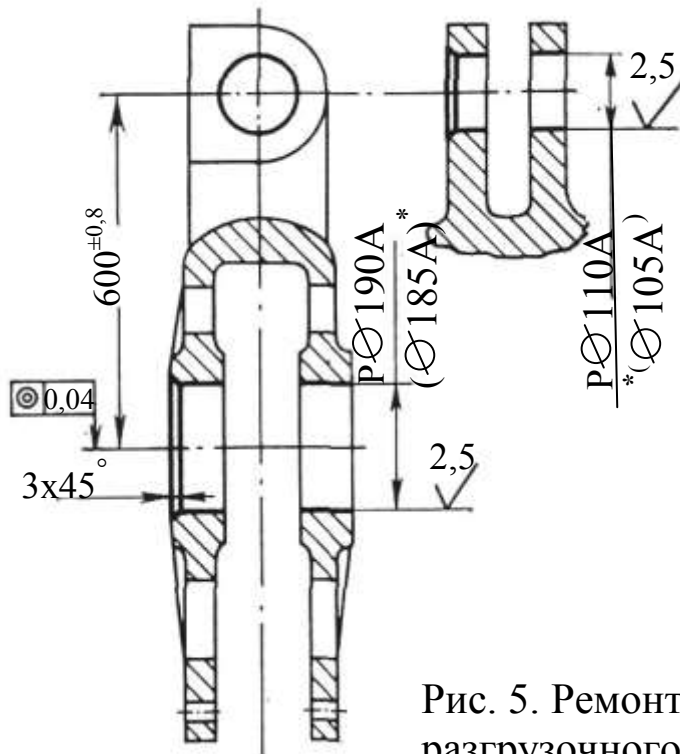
Ремонтный чертеж обоймы разгрузочного блока ковша:
